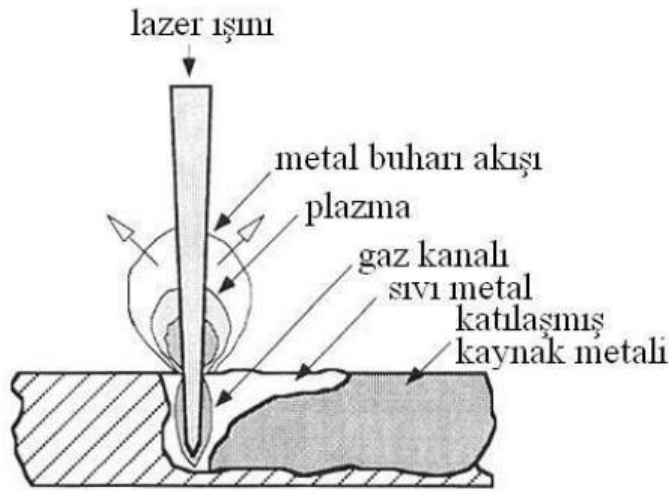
Kaynaklı birleştirmeler ile meydana gelen bölgeler (Atmaca, 2021)
